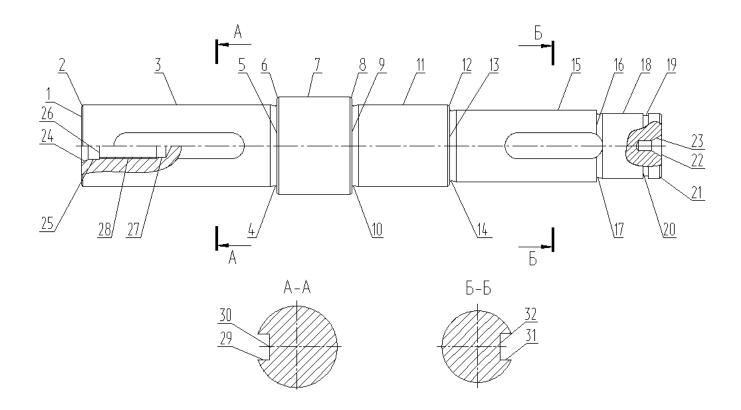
Систематизация поверхностей детали «Вал привода мотор-редуктора»
